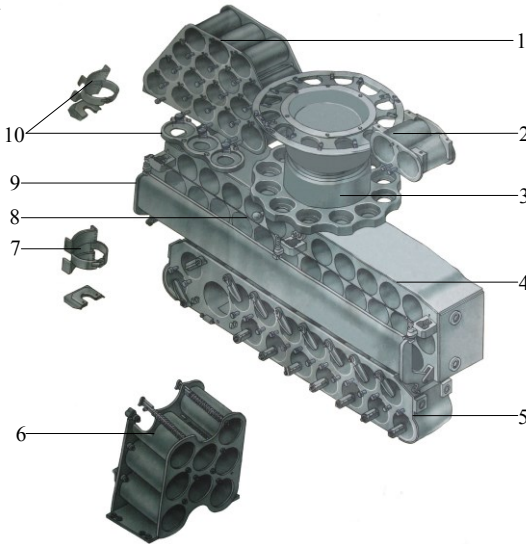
Боєукладка СГ 2С3М: 1 – укладка № 2; 2 – укладка № 3; 3 – карусельна укладка; 4 – щільникова укладка; 5 – укладка № 1; 6 – укладка; 7 – основа; 8 – рукоятка; 9 – плита; 10 – опора
